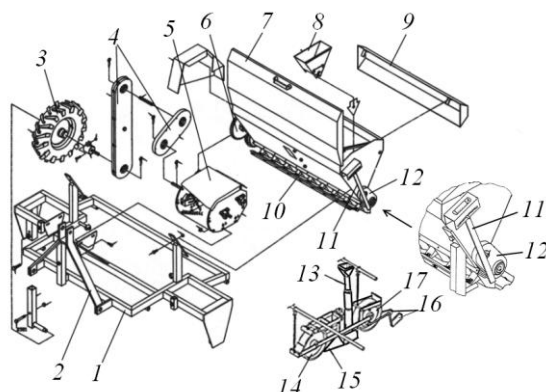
Детали и узлы сеялки «Эгедаль»: 1 – рама; 2 - навеска; 3 – приводное колесо; 4 - цепные передачи; 5 – многоступенчатый редуктор с 20-ю передачами 6 –зубчатая передача высевающего вала; 7 – бункер для семян; 8 – бункер для мелких семян; 9 – поддон; 10 – высевающий аппарат; 11 - рычаг регулировки размера щели высевающего аппарата; 12 – цепная передача привода ворошилки семян; 13 – семяпровод; 14 – направляющий каток; 15 – коробчатый сошник; 16 – загортач; 17 – уплотняющий каток
